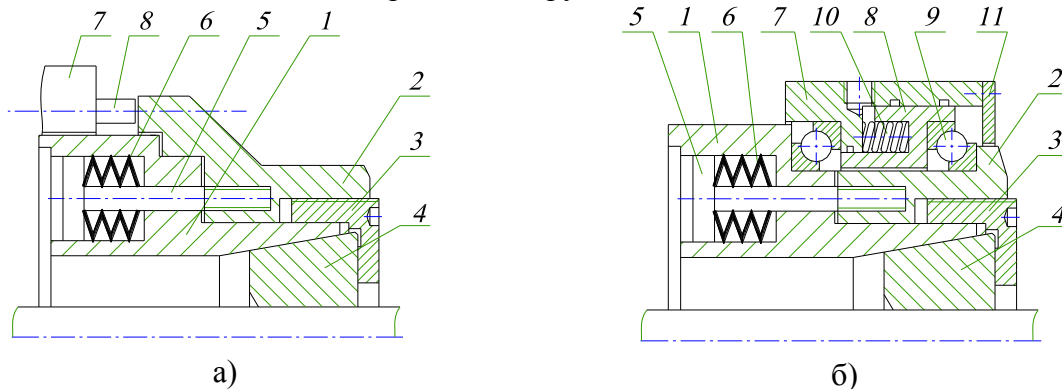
Затискні пристрої цангового типу для токарної обробки з інтегрованими пружинними приводами затиску та гідравлічними приводами розтиску
